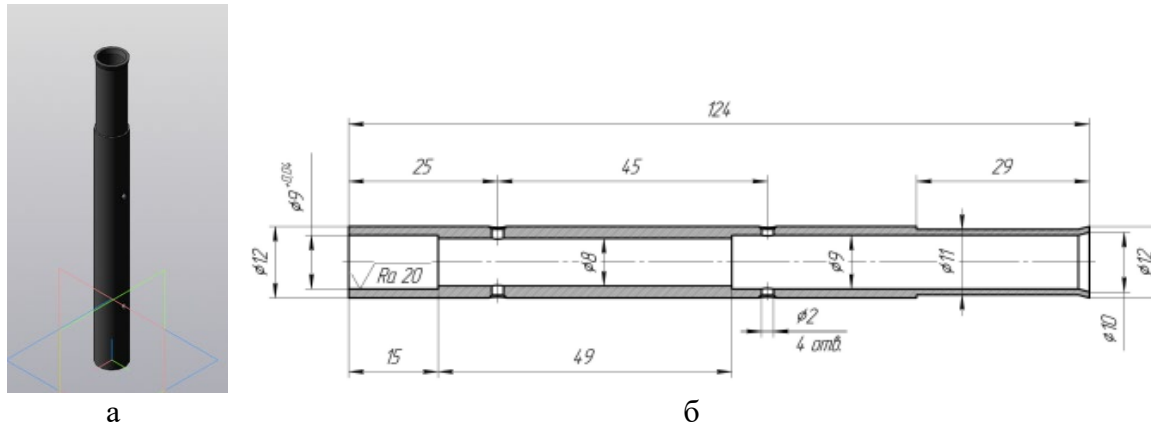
3D-модель (а) и фрагмент чертежа (б) трубки
